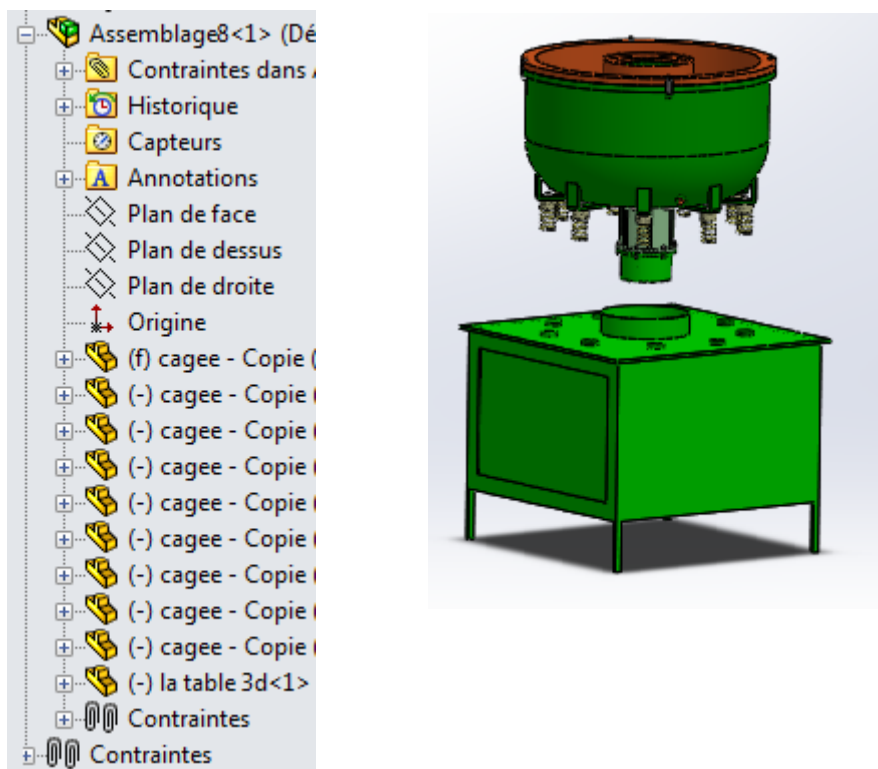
Les composantes du sous assemblage final dans une seule zone graphique
